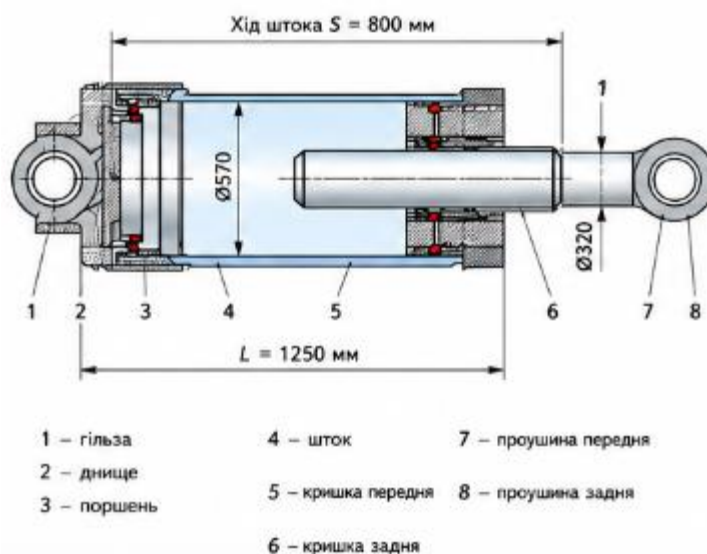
Загальний вигляд силового гідроциліндра преса Р6738В
